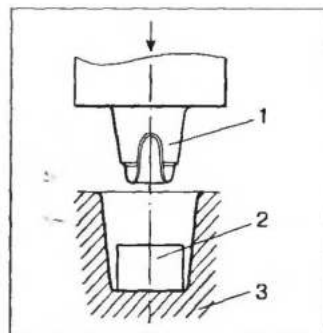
Схема штамповки заготовки поршня: 1 — пуансон; 2 — заготовка круглой формы; 3 — матрица
